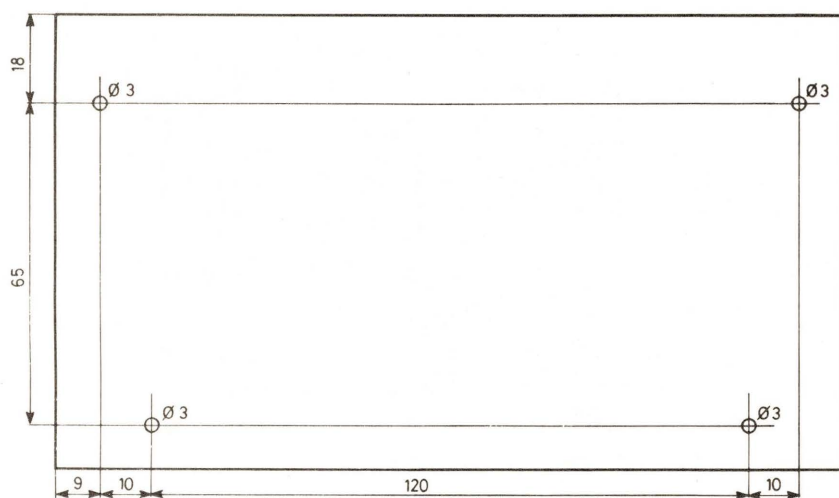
et 6. – Plan de perçage du fond du boîtier Teko P/3 et plan de câblage général du montage pourvu de dominos de raccordement.
